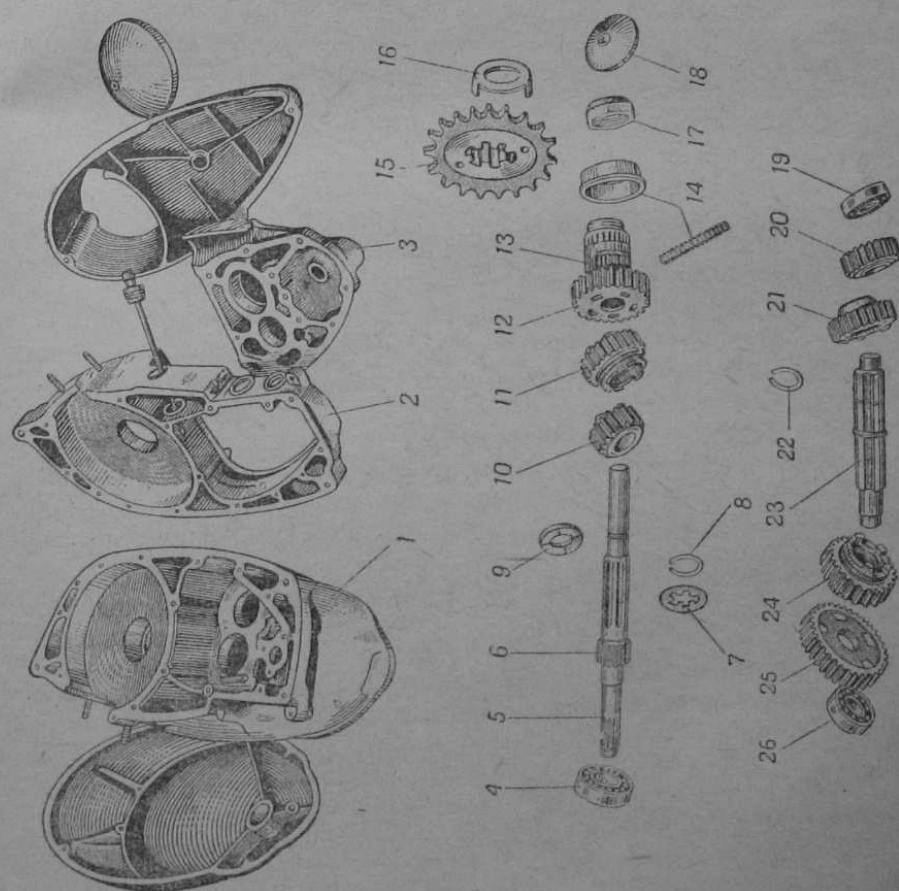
Коробка передач ИЖ-49 (ИЖ-350):
